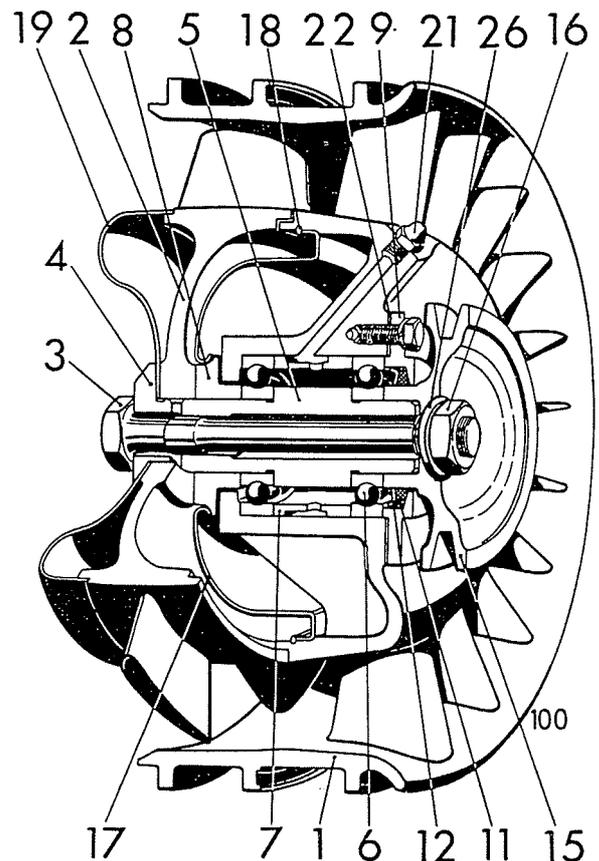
Kühlluftgebläse (zweiteilig) F/A1-2L 514
